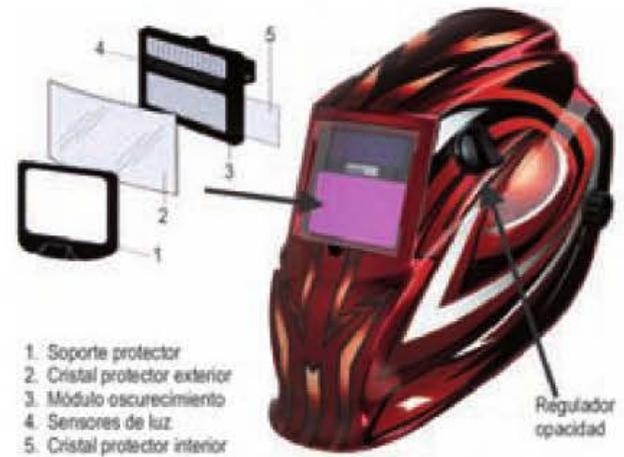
Pantalla de protección electrónica del soldador.
